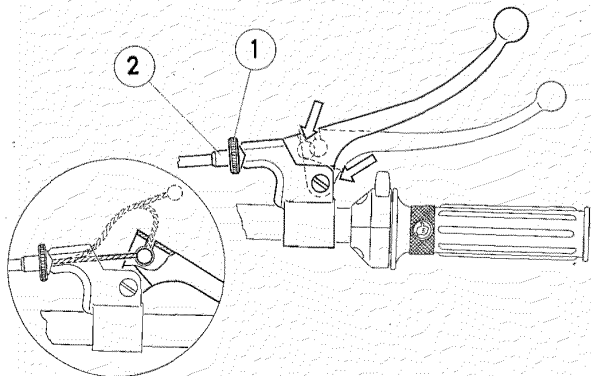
Mando freno delantero: Reglaje y engrase.
